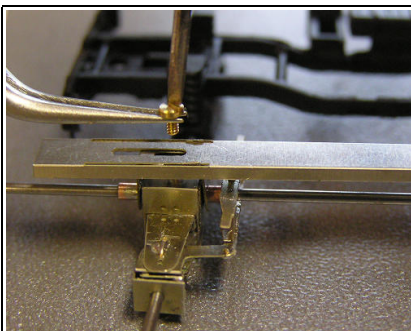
Die Vorderachse im Chassisblech mit der Schraube M1x2 befestigen.
